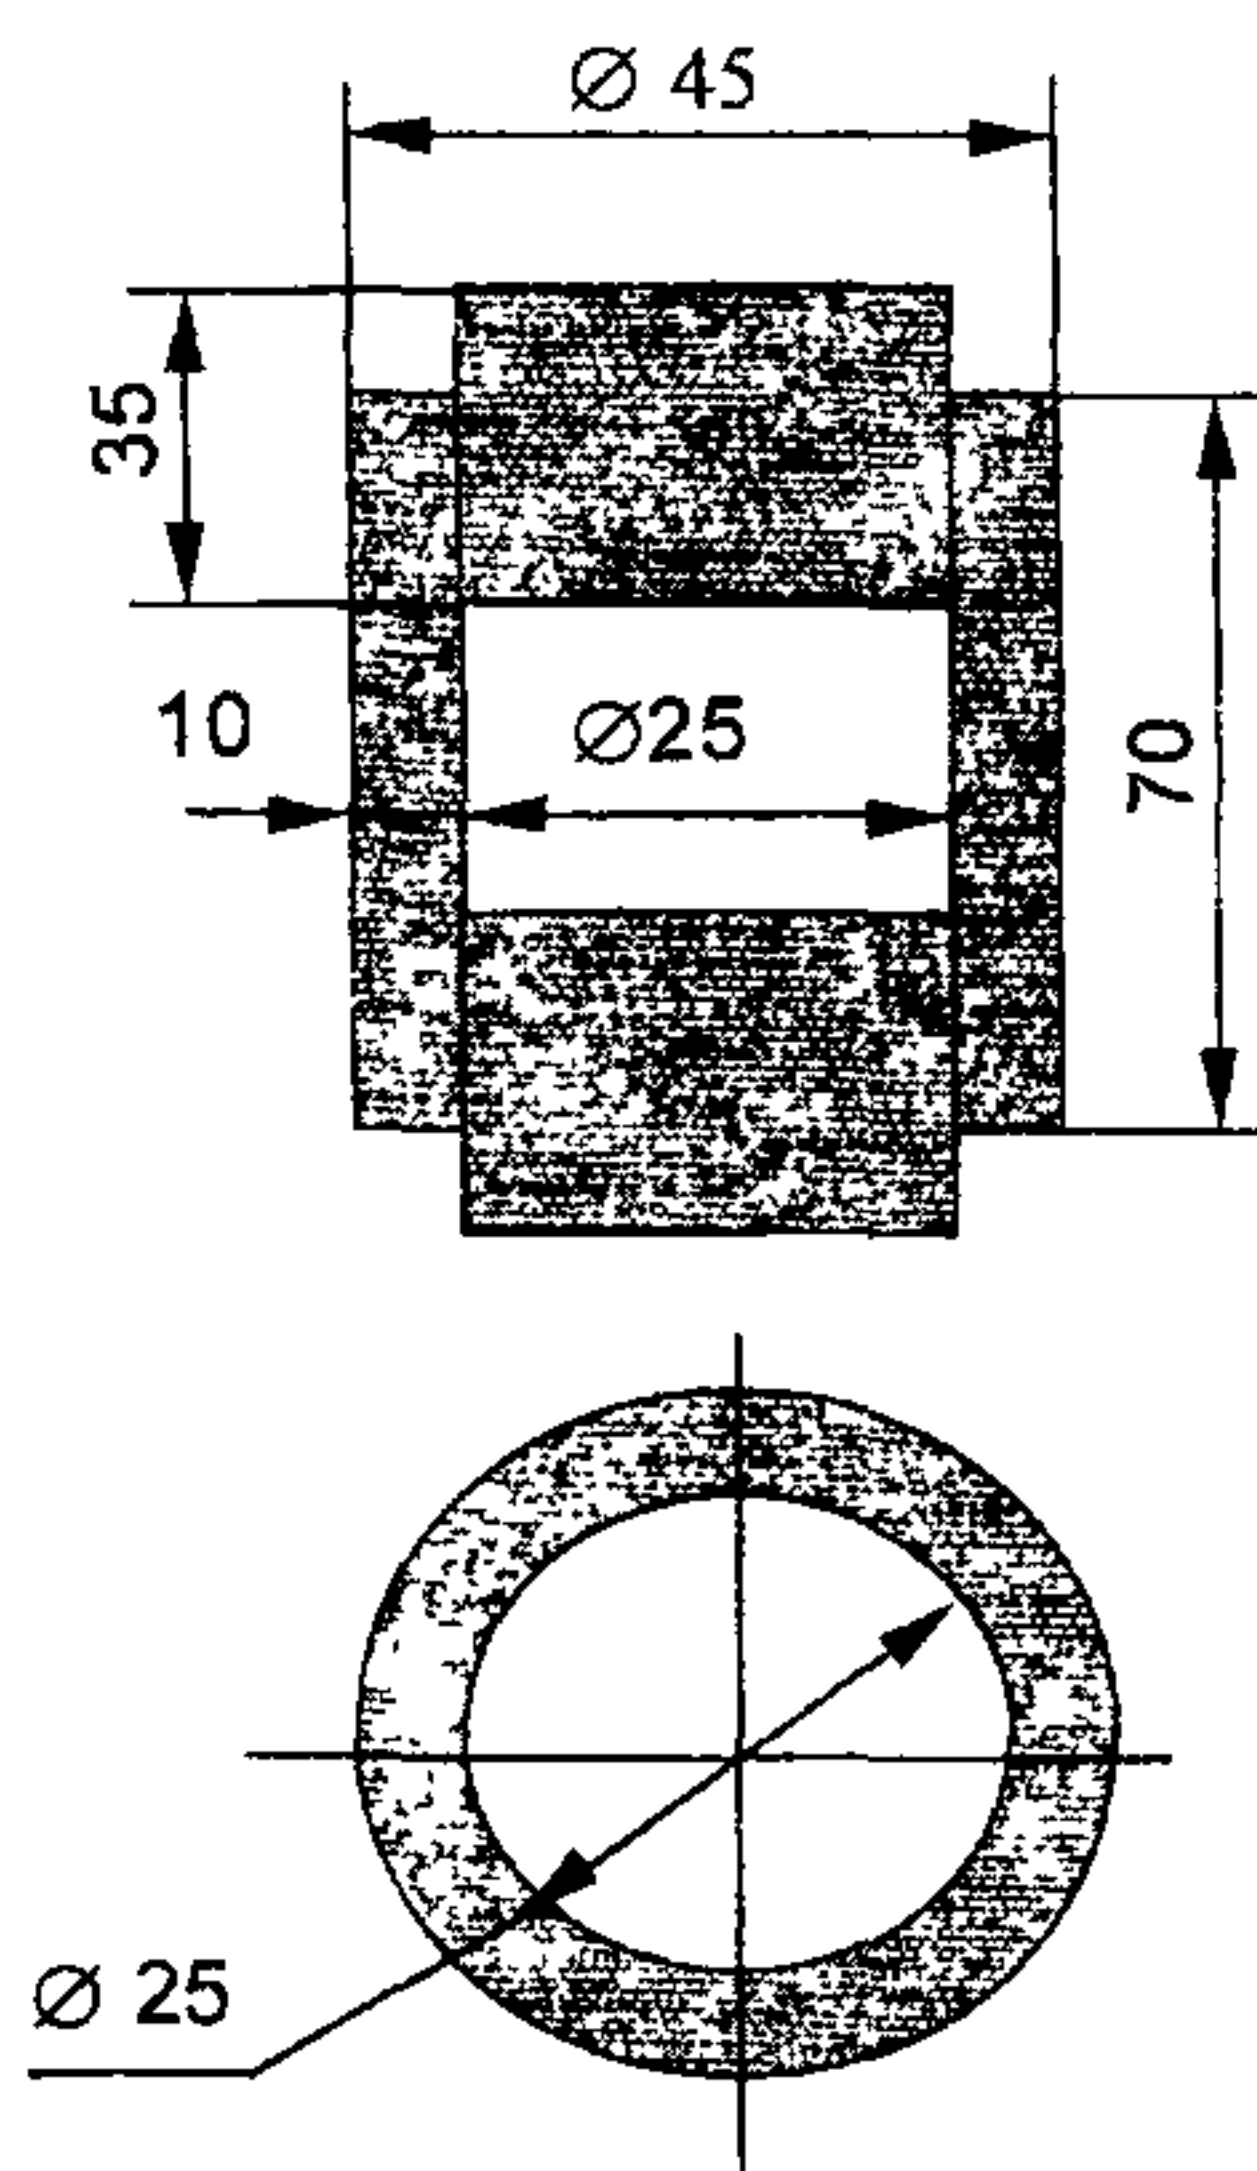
Металлическая форма для уплотнения образцов
